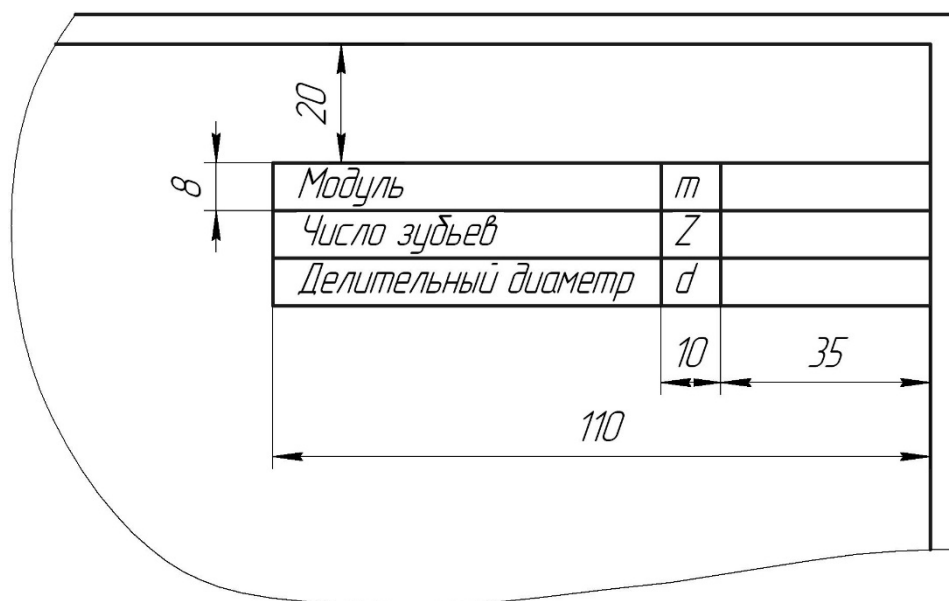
Таблица параметров для рабочего чертежа зубчатого колеса
